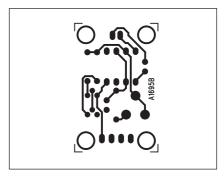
Obrazec desky spojů vysílače detektoru (strana TOP)
